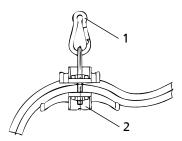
Fissaggio dei cavi di collegamento elettrici
